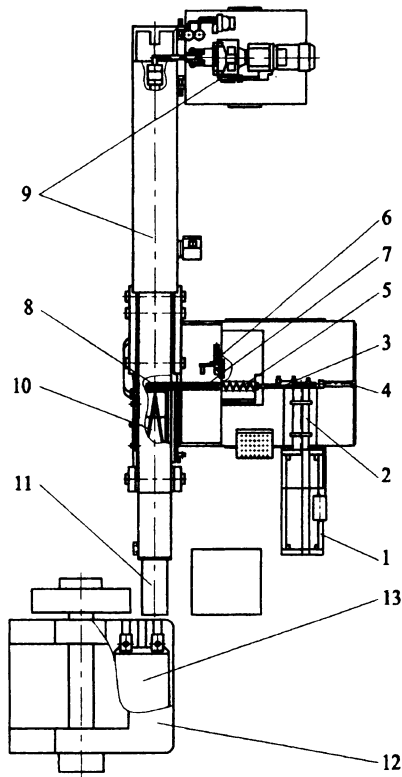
Специализированный штамповочный комплекс: 1 — элеваторное подающее устройство; 2 — наклонный накопительный лоток; 3 — горизонтальный призматический желоб; 4 — силовой цилиндр поштучного перемещения заготовок; 5 — индуктор; 6 — боковой толкатель; 7 — качающийся лоток; 8 — регулируемый упор; 9 — стан поперечно-клиновой прокатки; 10 — рабочий клиновой калибр; 11 — наклонный склиз; 12 — кривошипный пресс; 13 — специальный штамп
